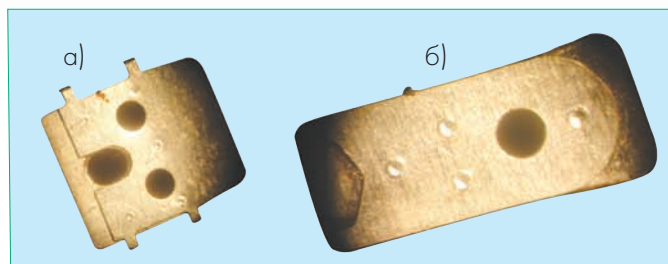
Лазерная сварка: а) коромысла с пластиной пятью точками; б) пружины с коромыслом четырьмя точками
